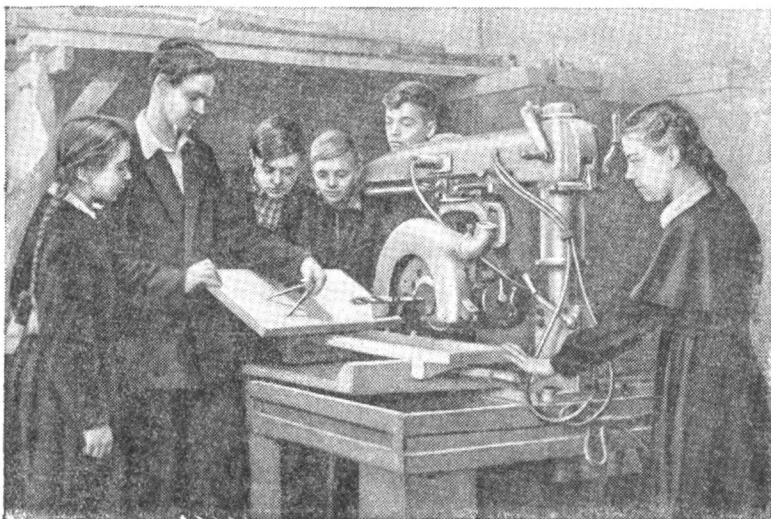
Школьники знакомятся с устройством универсального деревообрабатывающего станка.
